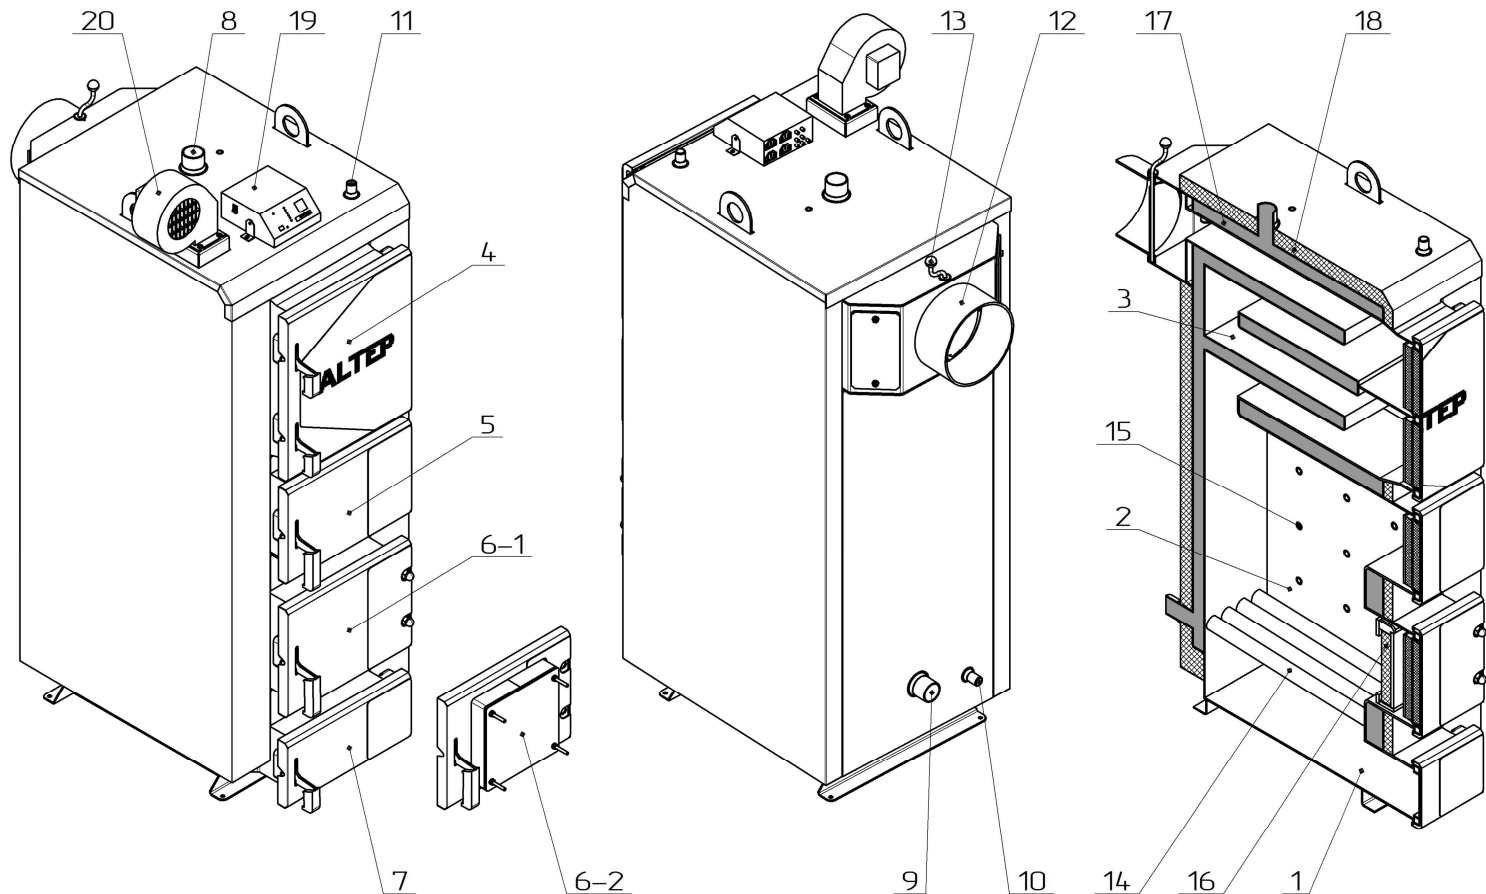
Габаритне креслення котла типу КТ-2Е-Н
